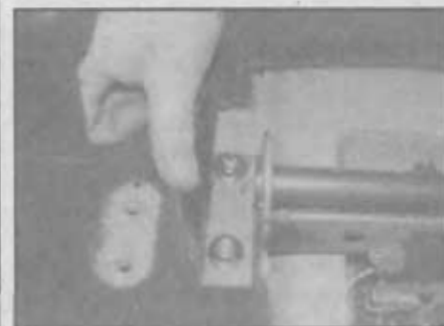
Расположение гаек крепления рычага стояночного тормоза
